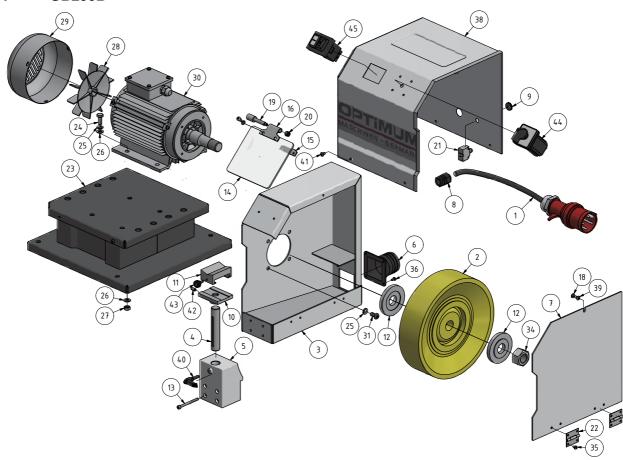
Ersatzteilzeichnung - Spare parts drawing
